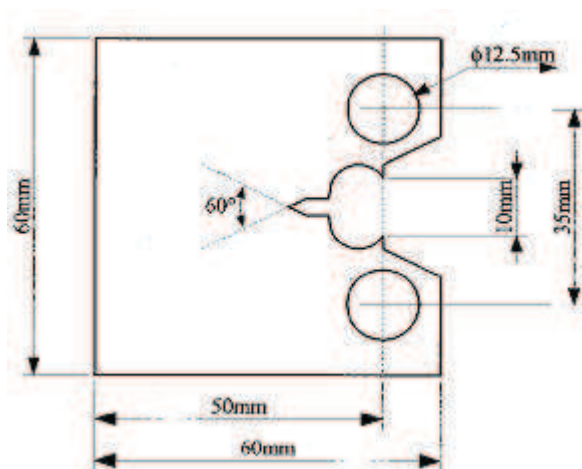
Plan d'une éprouvette CT25 (Prabel, 2007)
